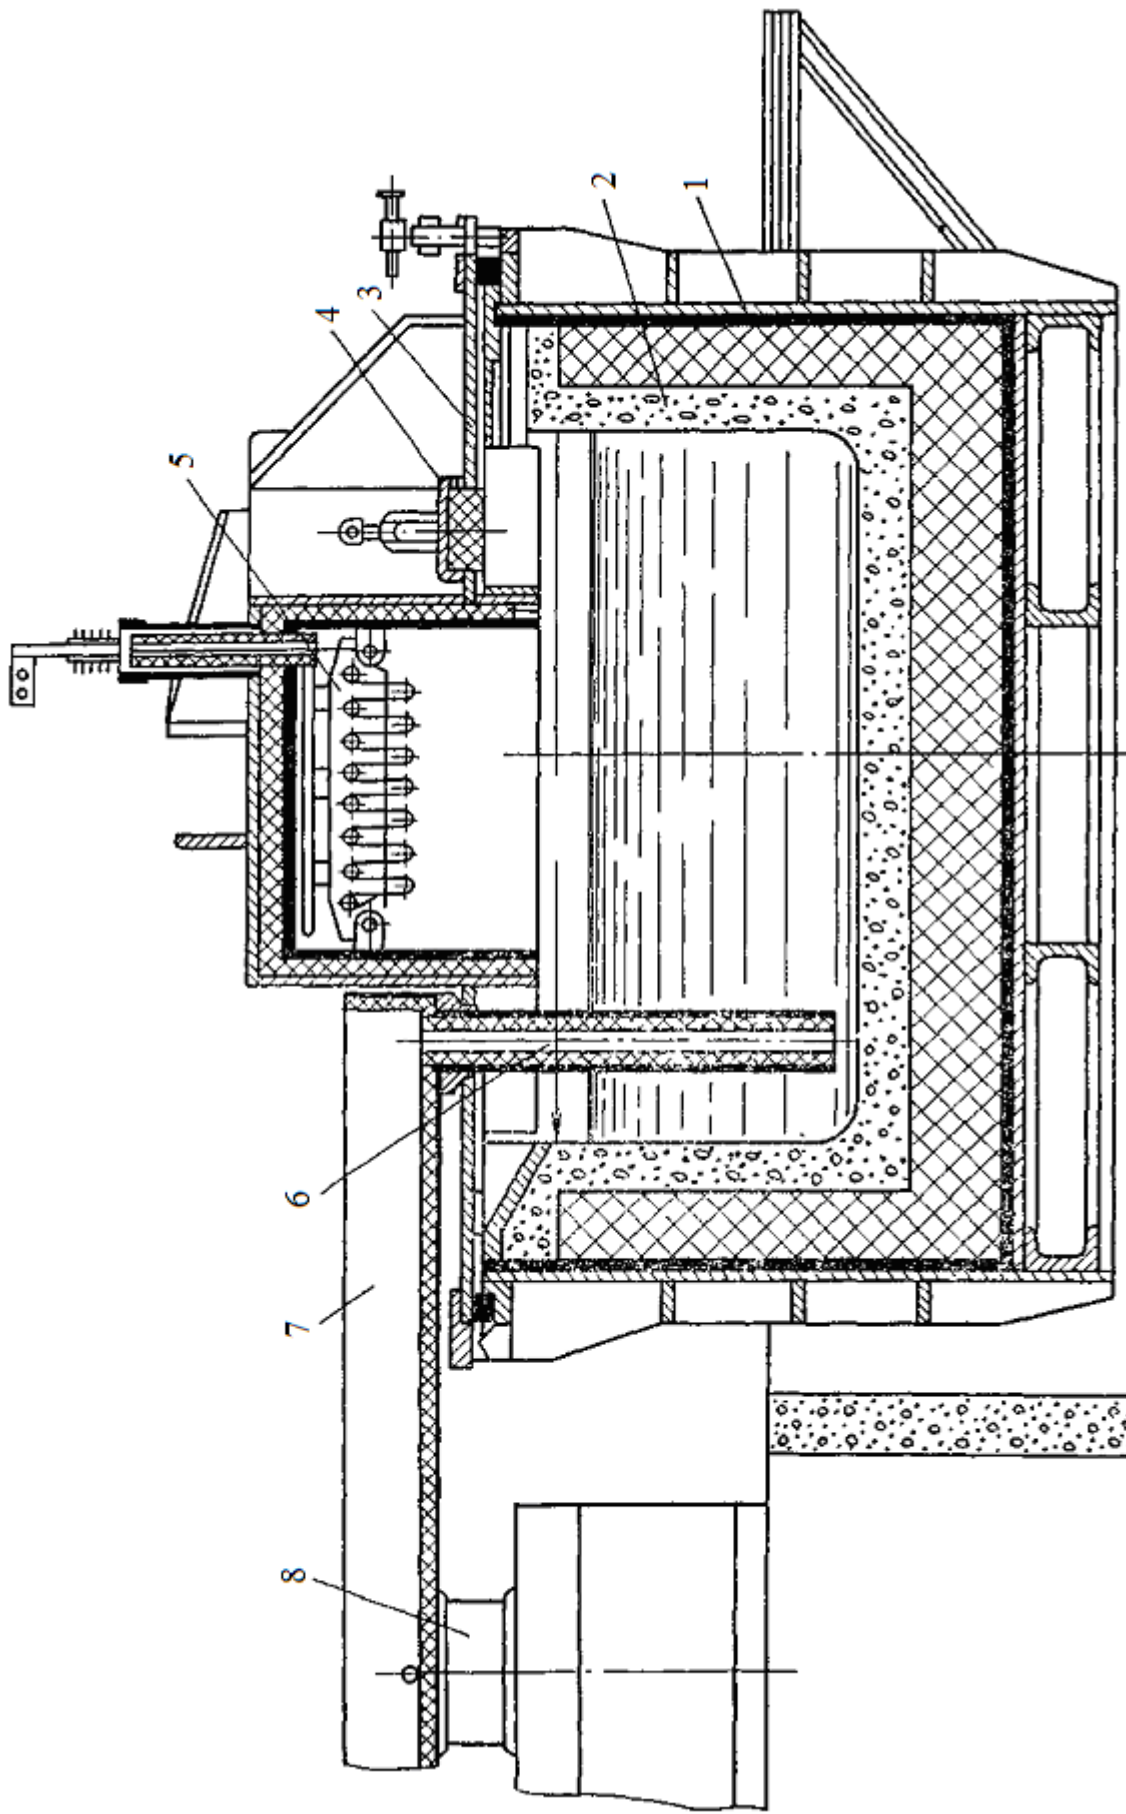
Схема вакуумного миксера: 1 – стальной корпус; 2 – футеровка из жароупорного бетона; 3 – крышка; 4 – люк для установки мешалки; 5 – нагреватель; 6 – литейная труба; 7 – распределитель металла; 8 – кристаллизатор
